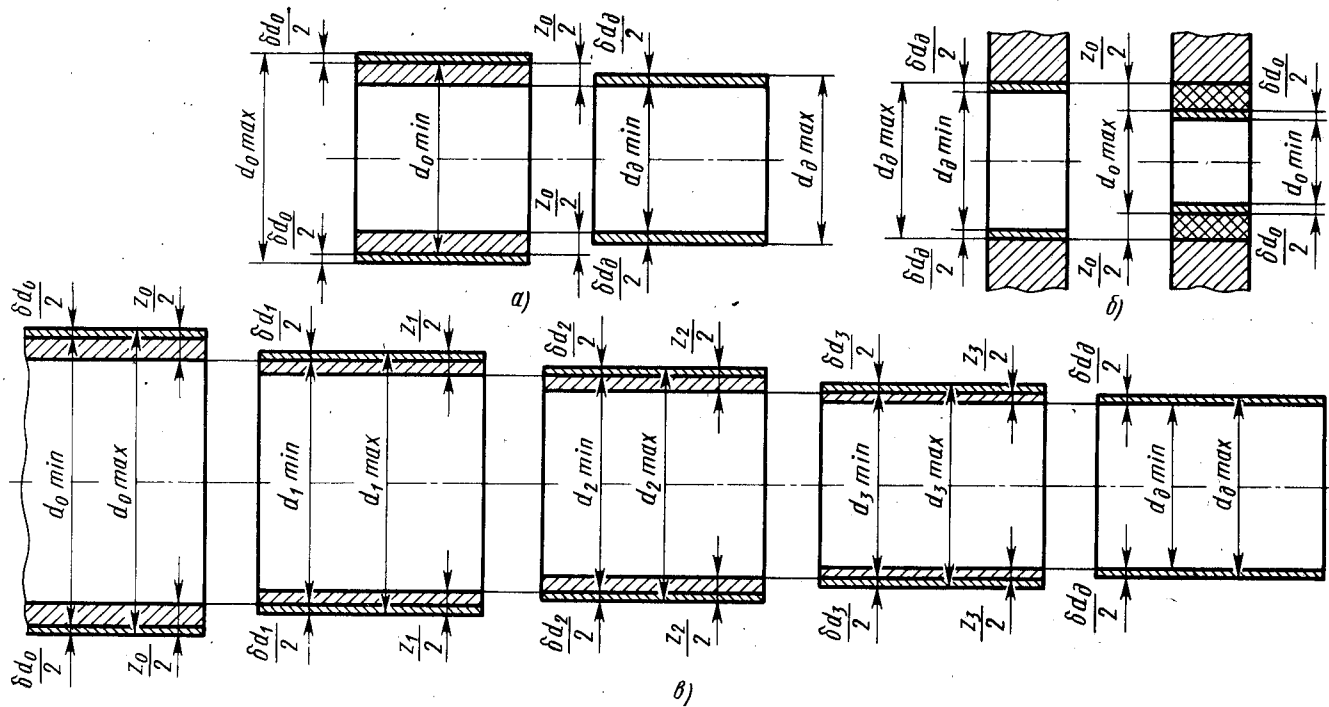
Схема расположения межоперационных припусков и допусков
